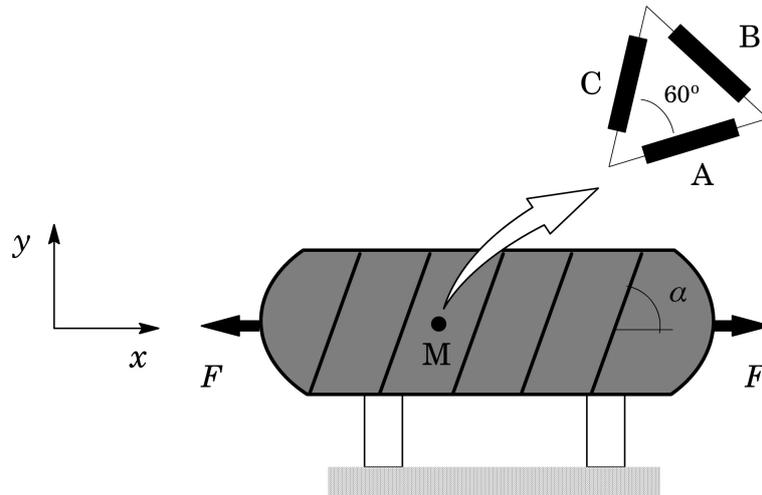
Tanque de aço soldado com costura espiral.
